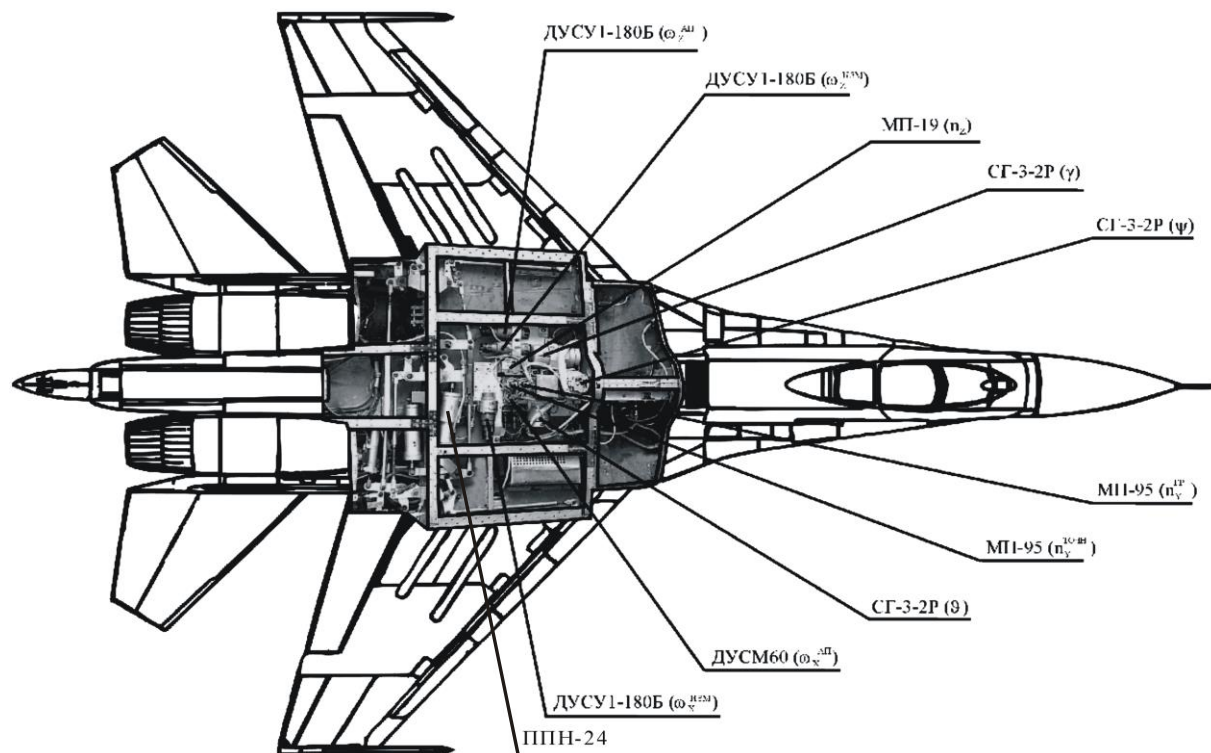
Схема размещения приборного и агрегатного оборудования СЛМТ-10
